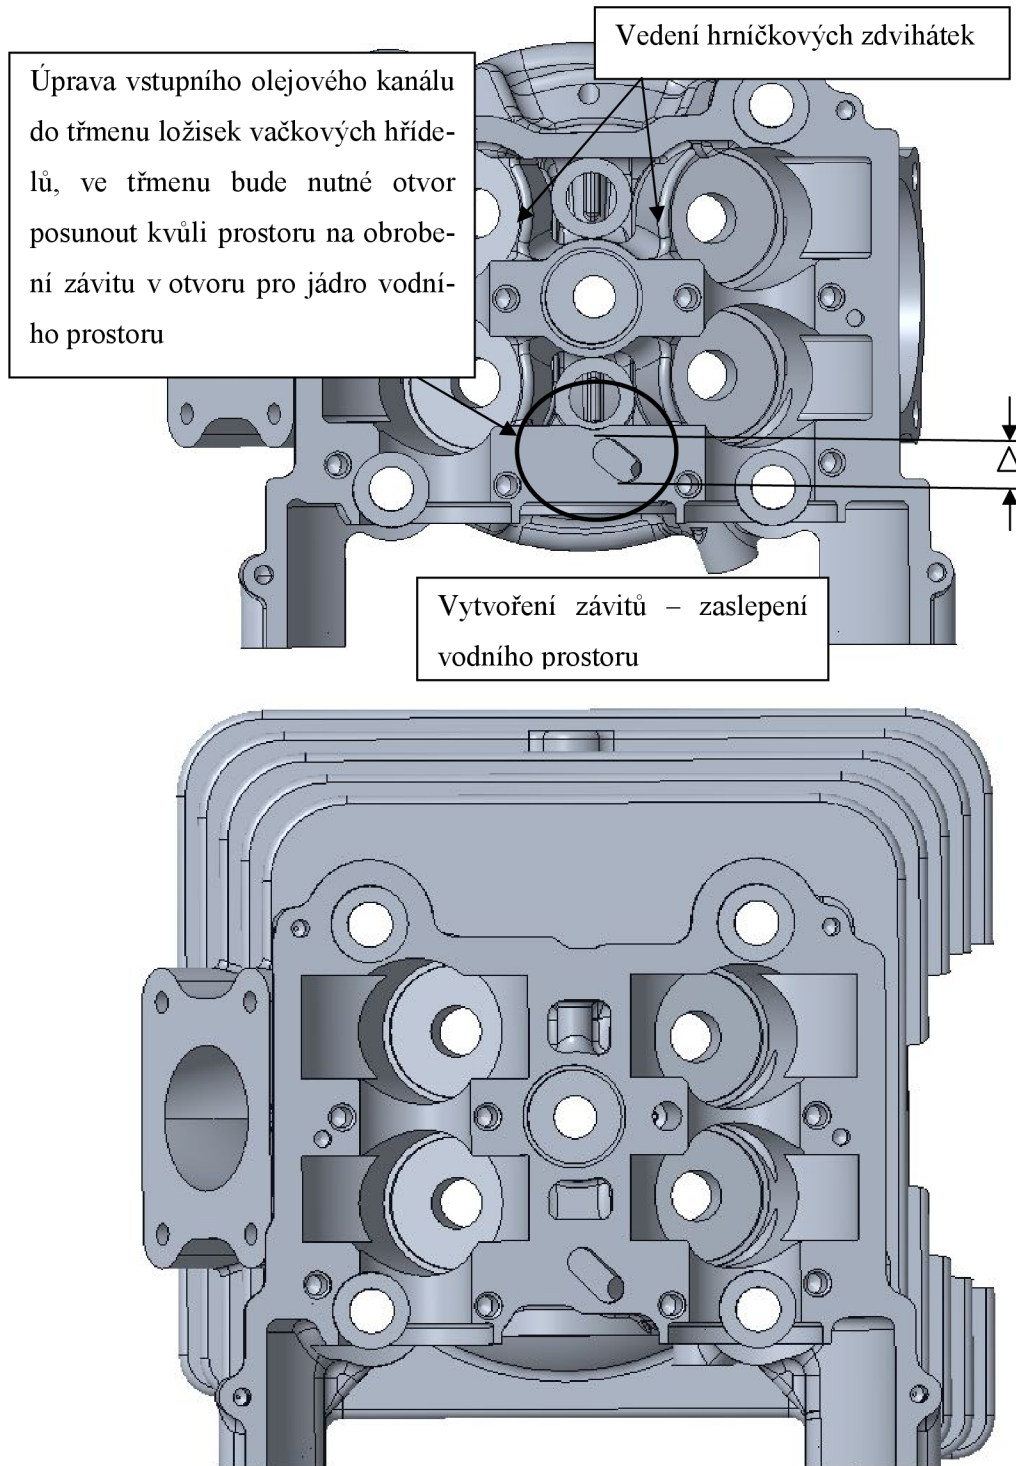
Přívodní a odvodní motorového oleje z kapalinou chlazené hlavy
